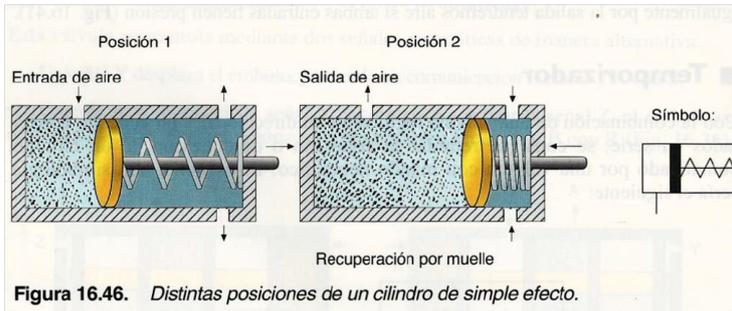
Distintas posiciones de un cilindro de simple efecto.
